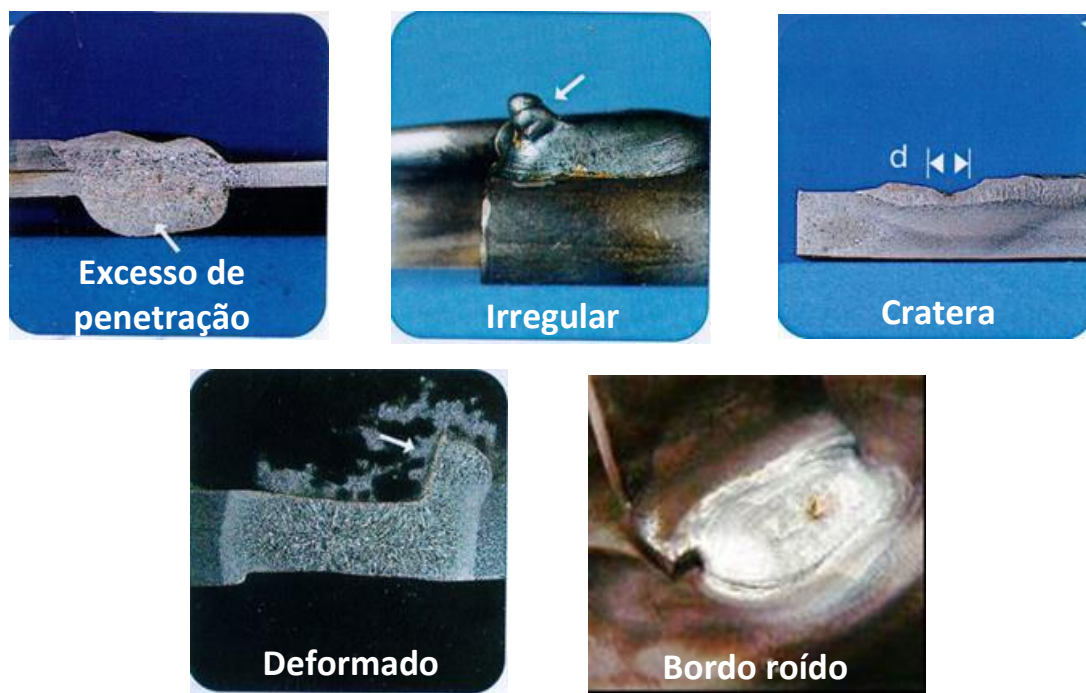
Outros tipos de defeitos de soldadura [Fonte: Documentação interna da Empresa].
